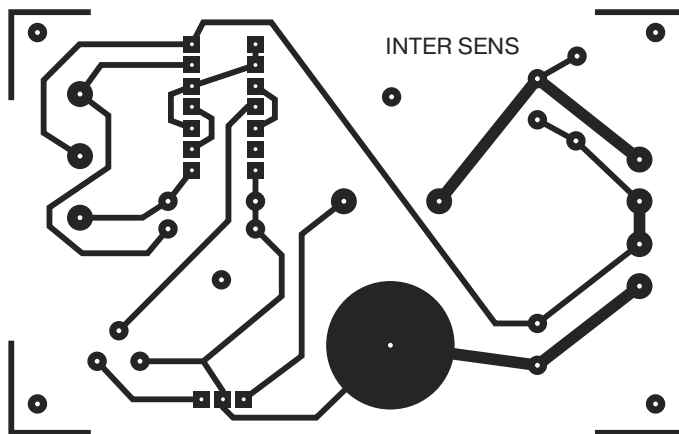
Чертеж печатной платы сенсорного выключателя
